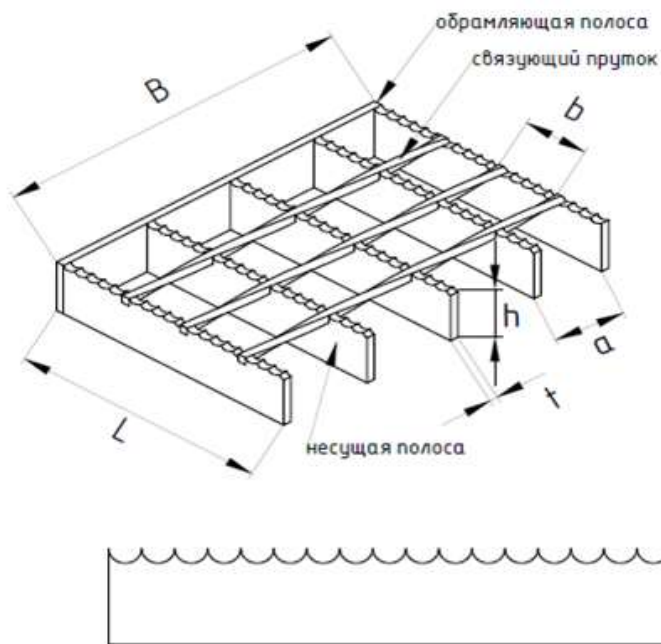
Схема сварного настила с противоскольжением
